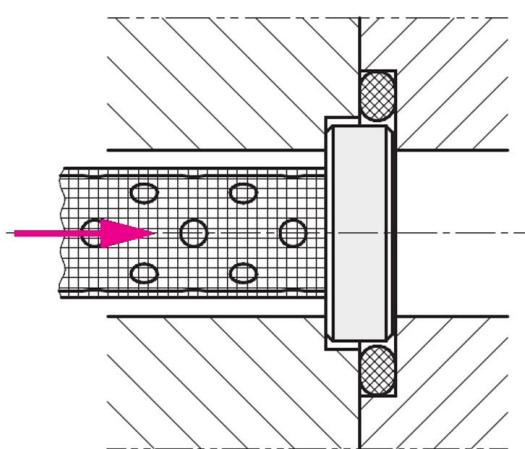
Ejemplo de montaje de filtro insertable de presión 3887066
